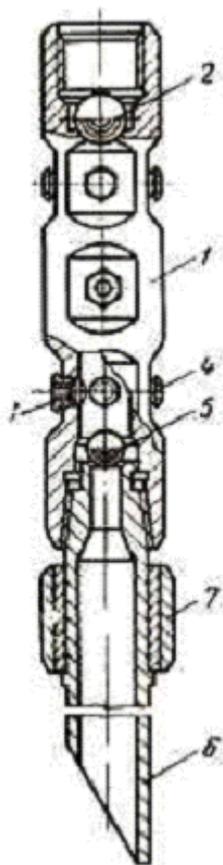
Аппарат для гидро-пескоструйной перфорации АП-6М: 1 - корпус; 2 - шар опрессовочного клапана; 3 - узел насадки; 4 - заглушка; 5 - шар клапана; 6 - хвостовик; 7 - центратор
